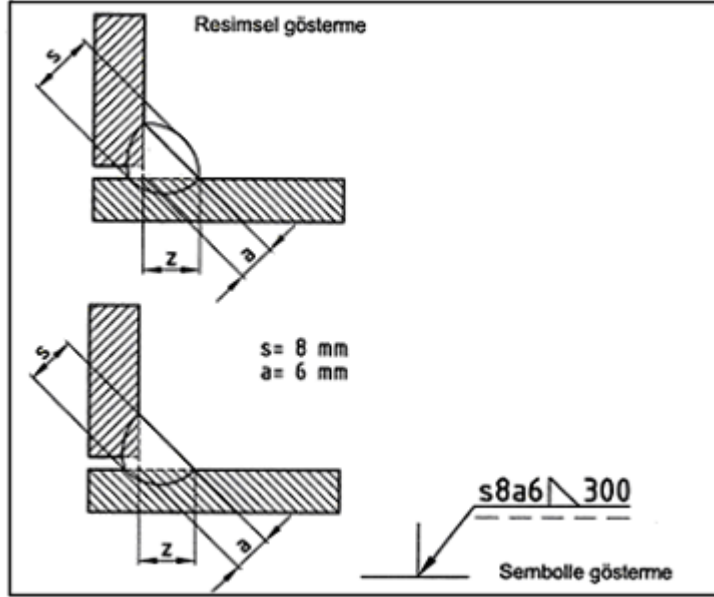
Kaynak dikişi sembolü ve ilave edilen ölçüler
